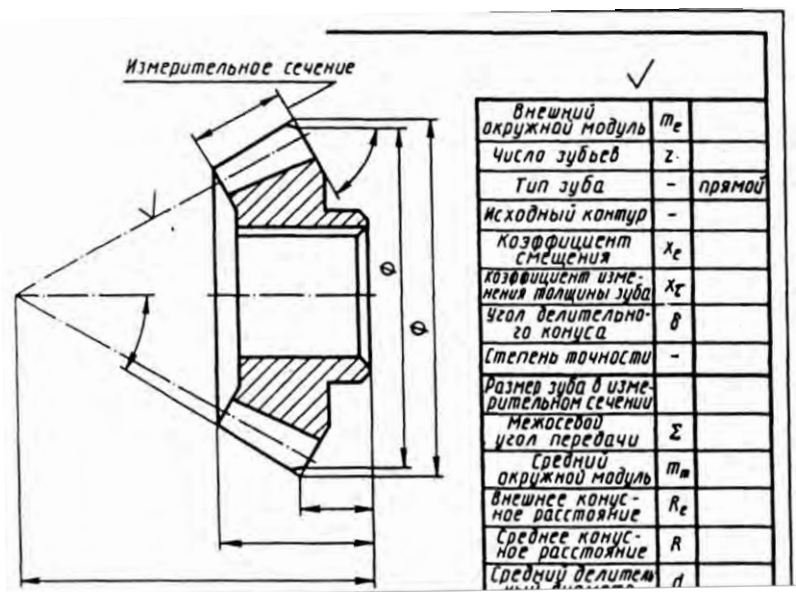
Пример указания параметров зубчатого венца прямозубого конического зубчатого колеса
